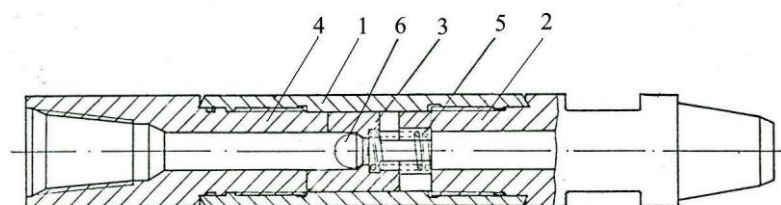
Противоаварийный забойный разъединитель ПЗР-Б
